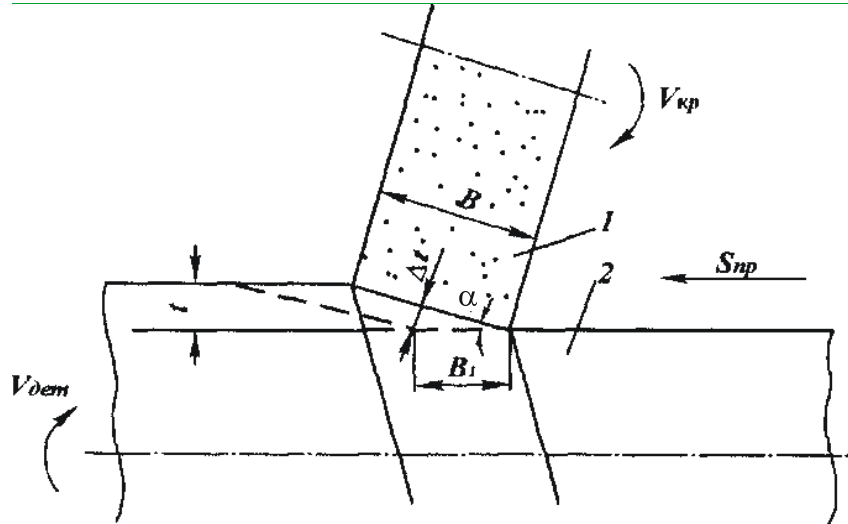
Расчетная схема круглого наружного продольного глубинного шлифования: 1 – круг; 2 – деталь
